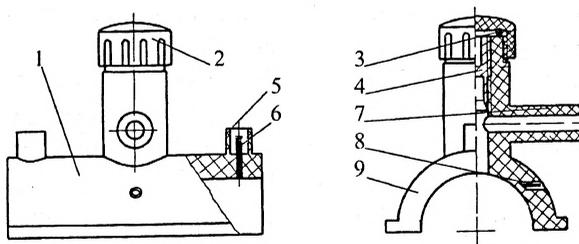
Конструкция фитинга седлового: 1 — полиэтиленовый корпус, 2 — полиэтиленовая крышка, 3 — резиновое уплотнительное кольцо, 4 — металлический резак, 5 — защитная втулка, 6 — клемма, 7 — отводной патрубок, 8 — индикатор сварки, 9 — присоединительная поверхность
